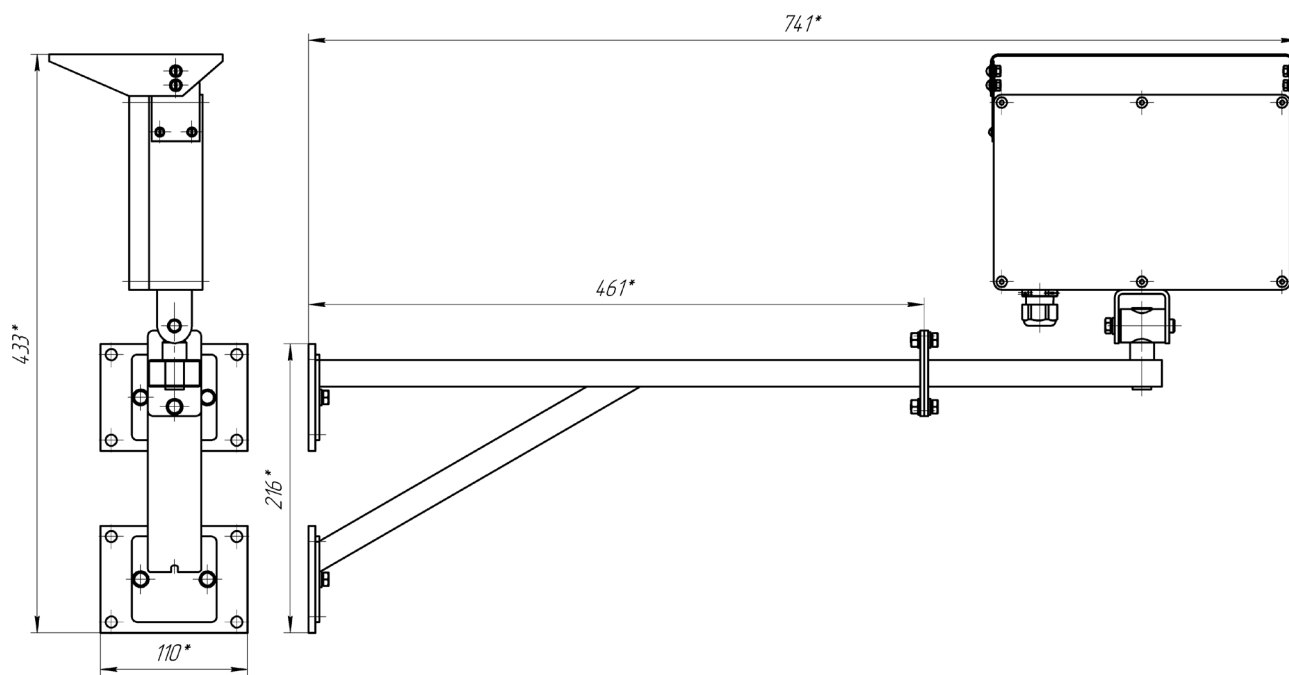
Габаритные размеры извещателя с КМ4.
